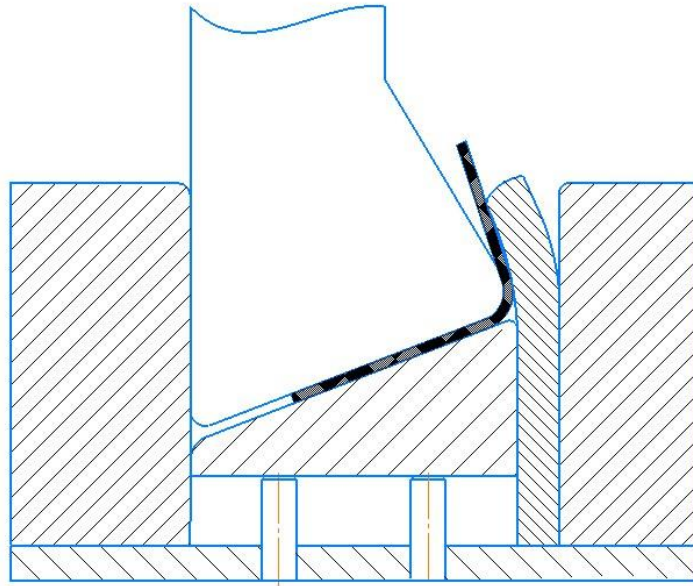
Схема гибки V-образной детали с угломгиба не более 90°
